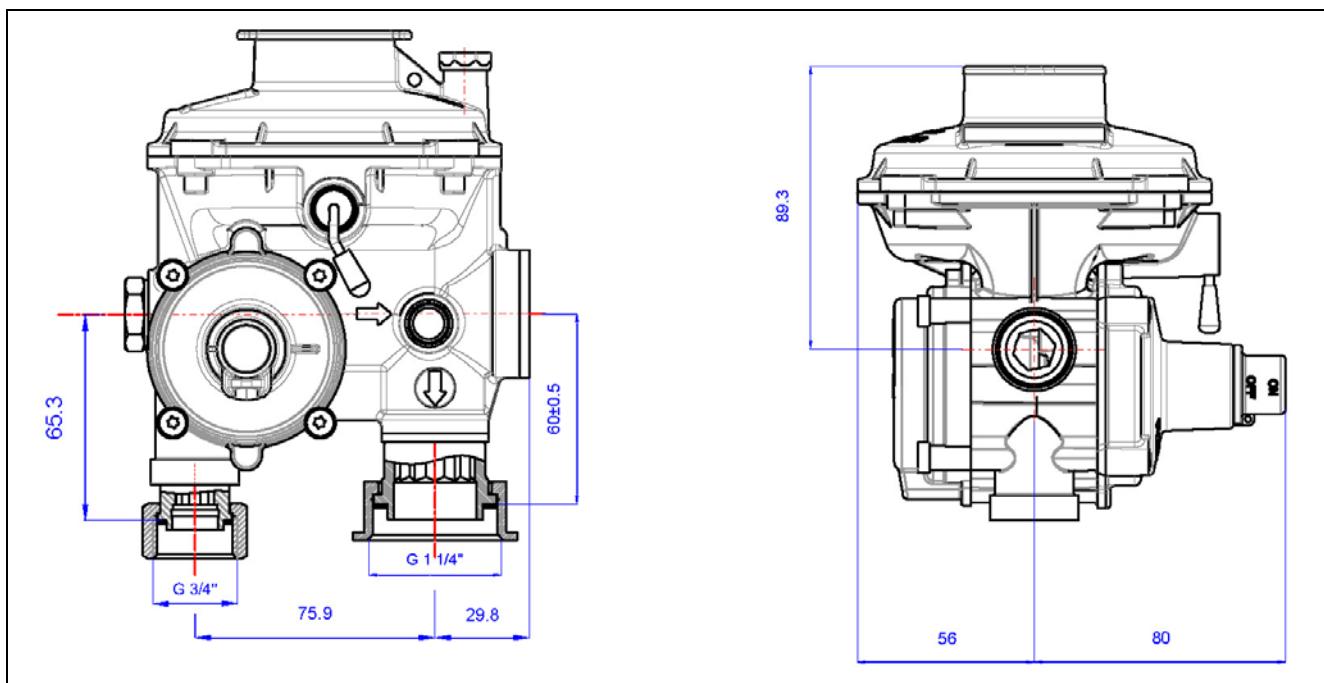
Габаритные и присоединительные размеры регулятора давления РД с входом и выходом, направленными вниз
